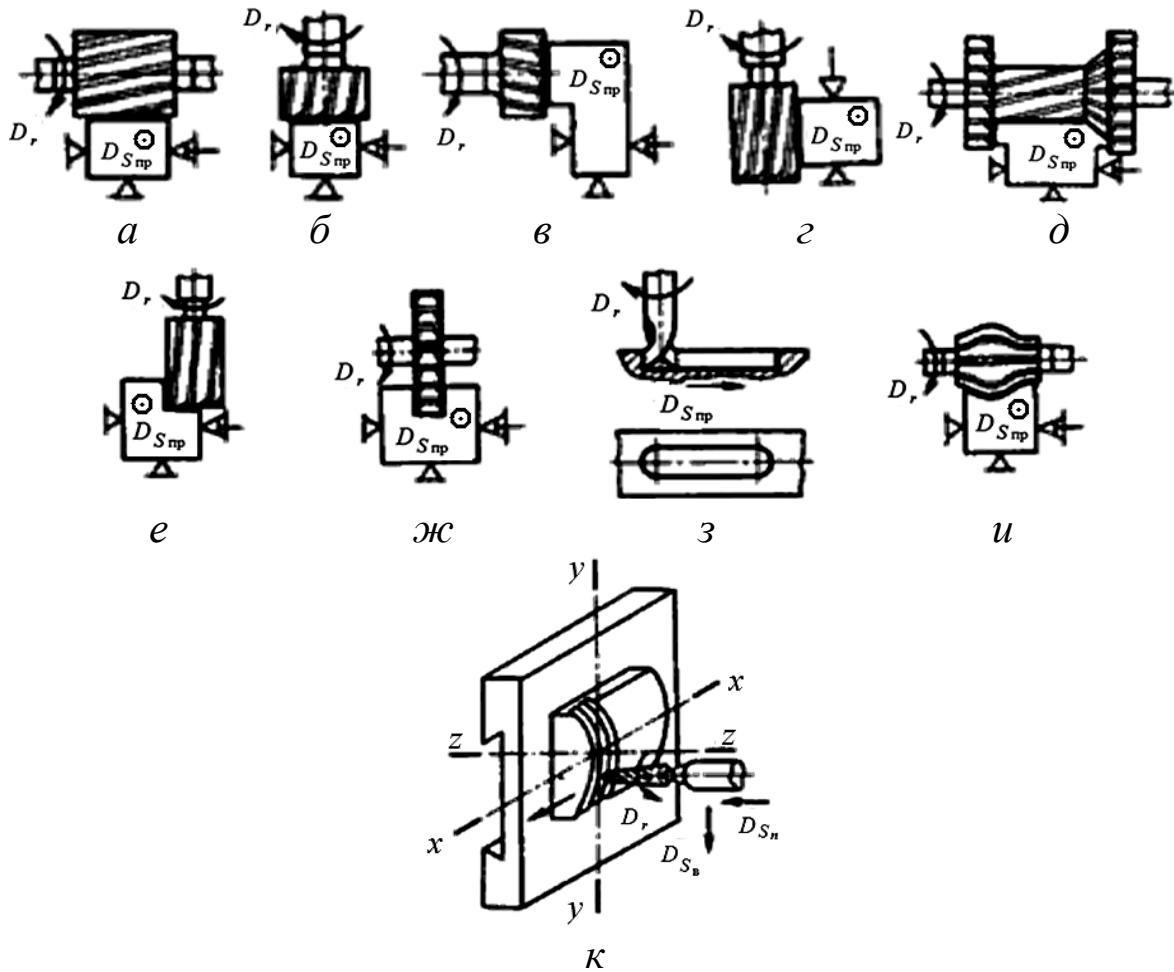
Схемы обработки заготовок на станках фрезерной группы
